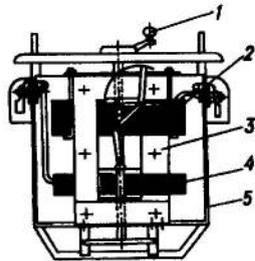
Пересувний зварювальний трансформатор ТД-102
